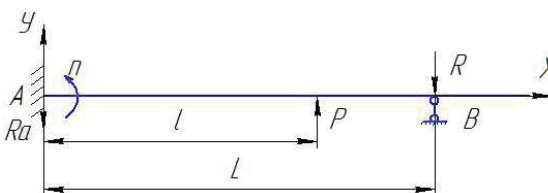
Схема токарной обработки заготовки чашечным резцом
